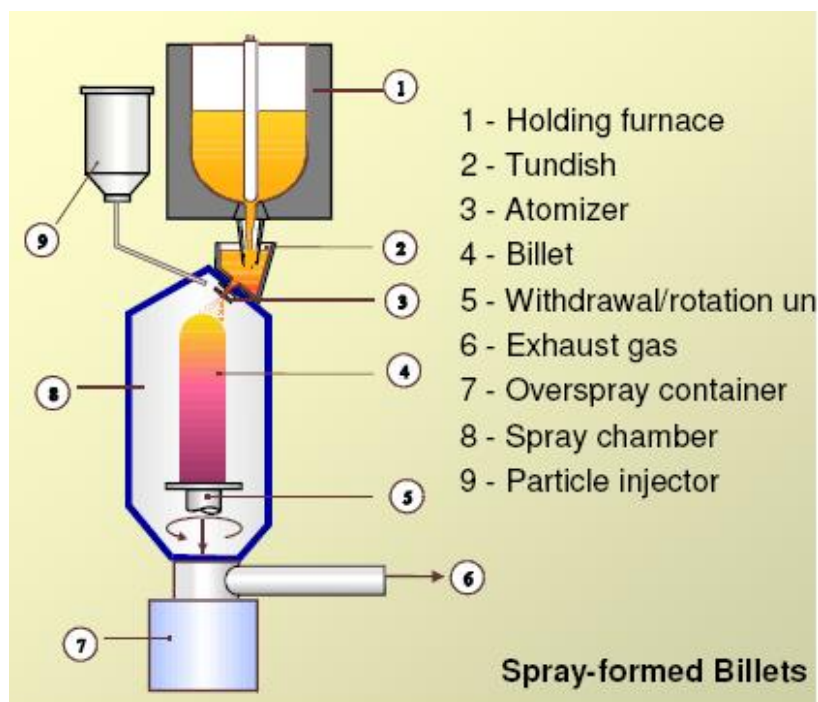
Схема технологии *Spray forming*: 1 – тигель, 2 – сливное устройство; 3 – подвод газа, 4 – выращиваемая болванка, 5 – вращающаяся подложка; 6 – отвод газа; 7 – бункер для порошка; 9 – (опция) бункер для подшихтовки дополнительного материала
